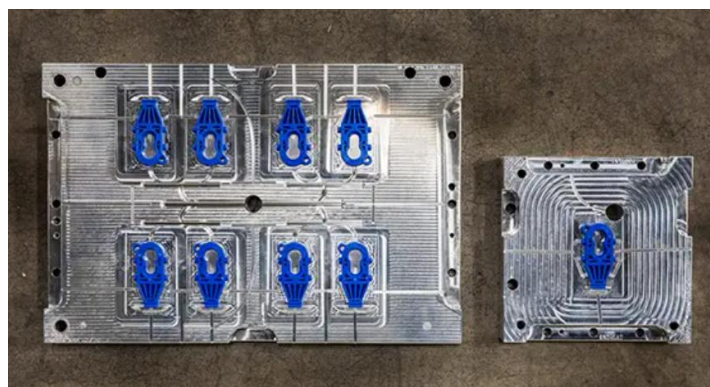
1 Comparación entre un molde multicavidad (izquierda) y un molde con una única cavidad (derecha) [10]
